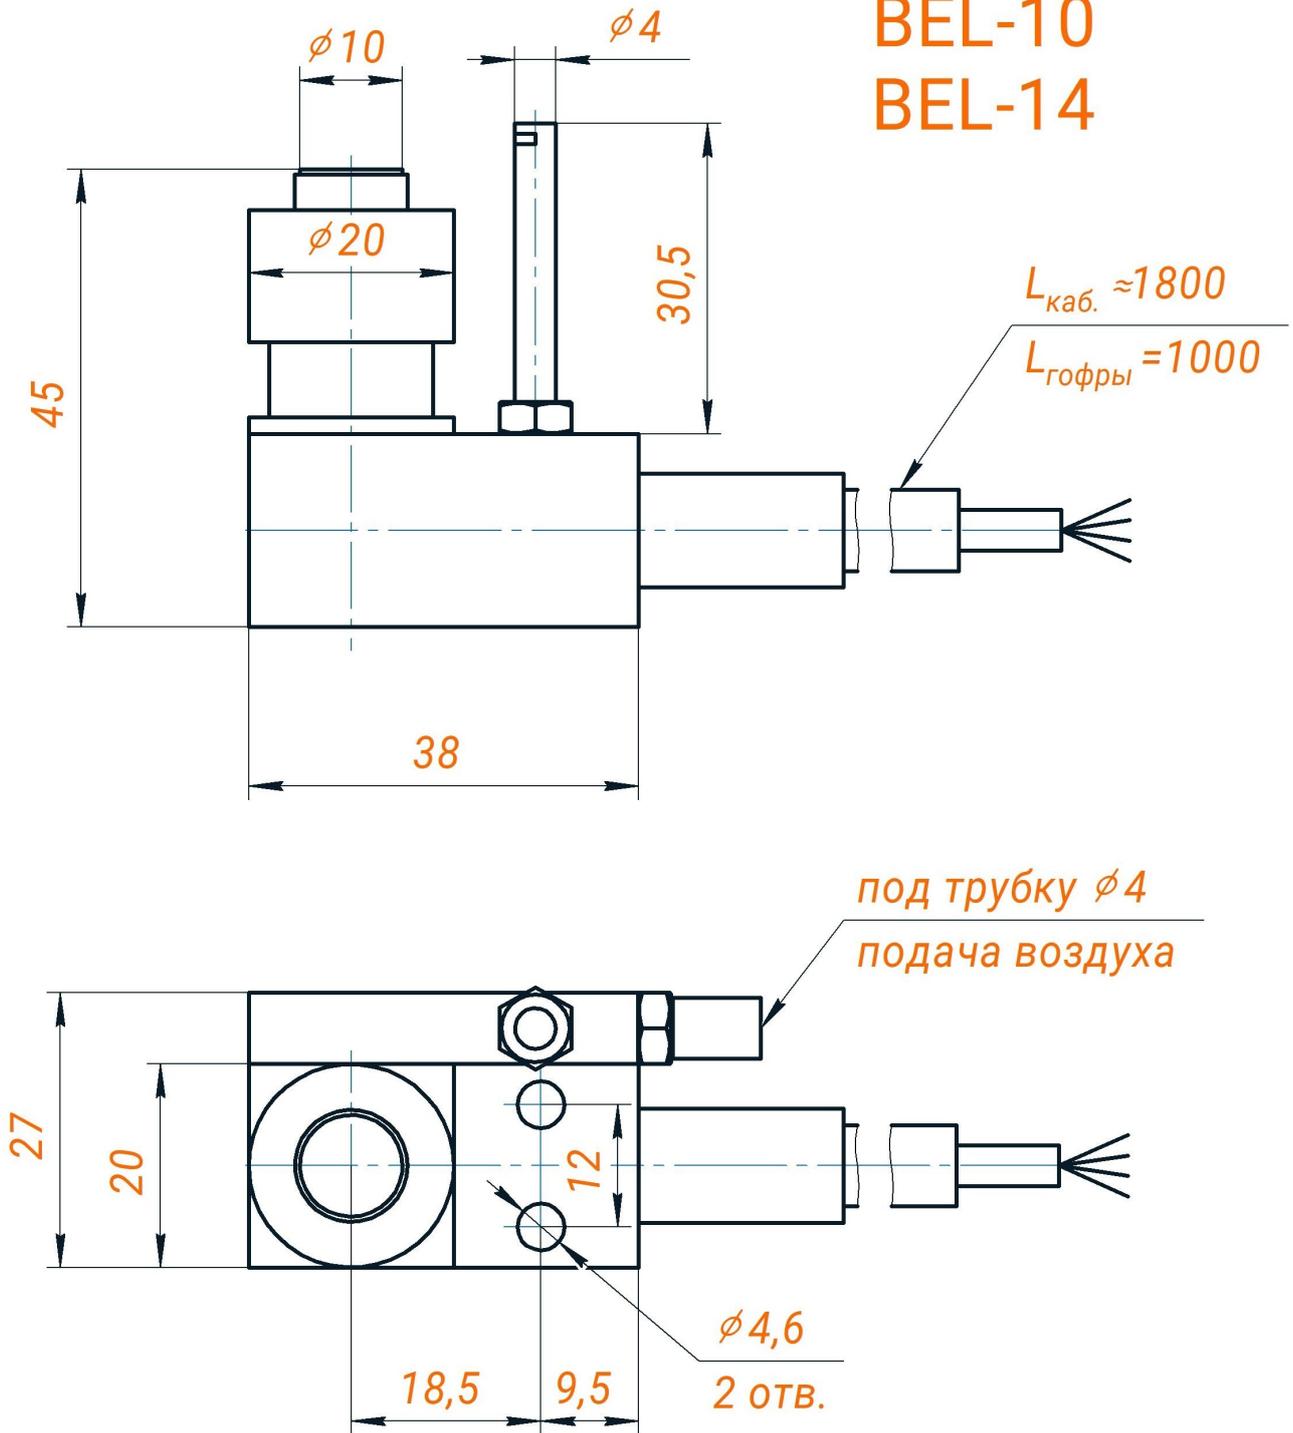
Габаритные размеры датчиков BEL-10 и BEL-14
